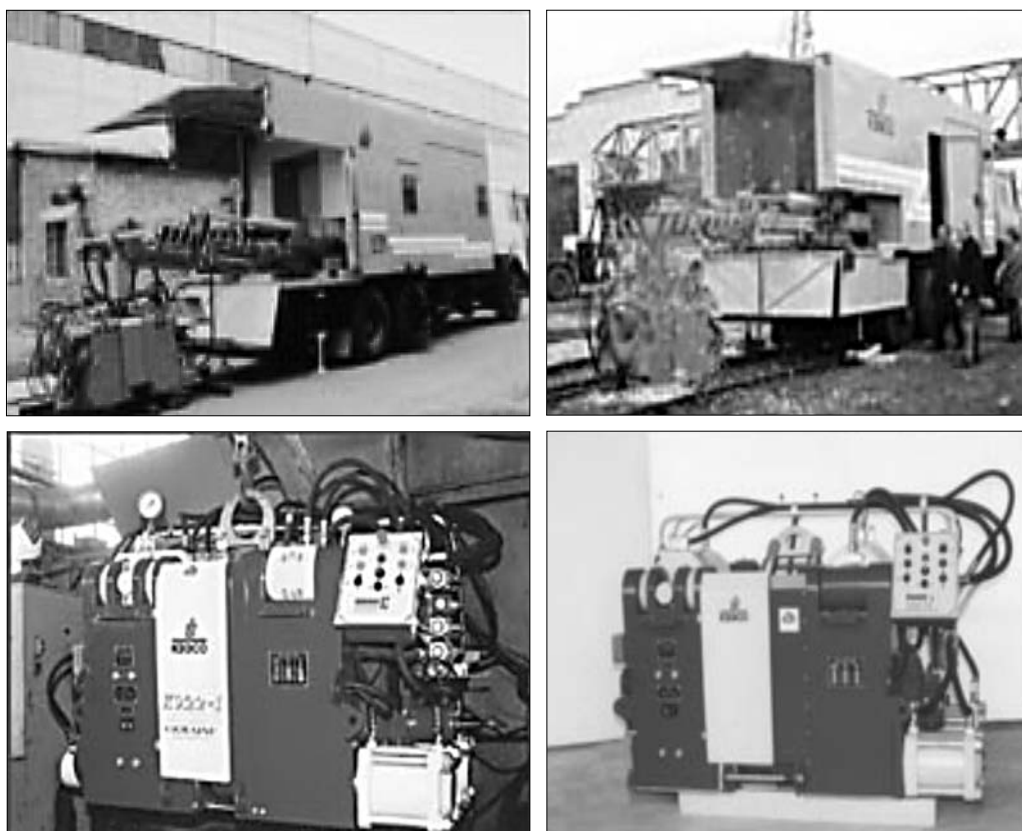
Современные машины для контактной сварки высокопрочных железнодорожных рельсов
